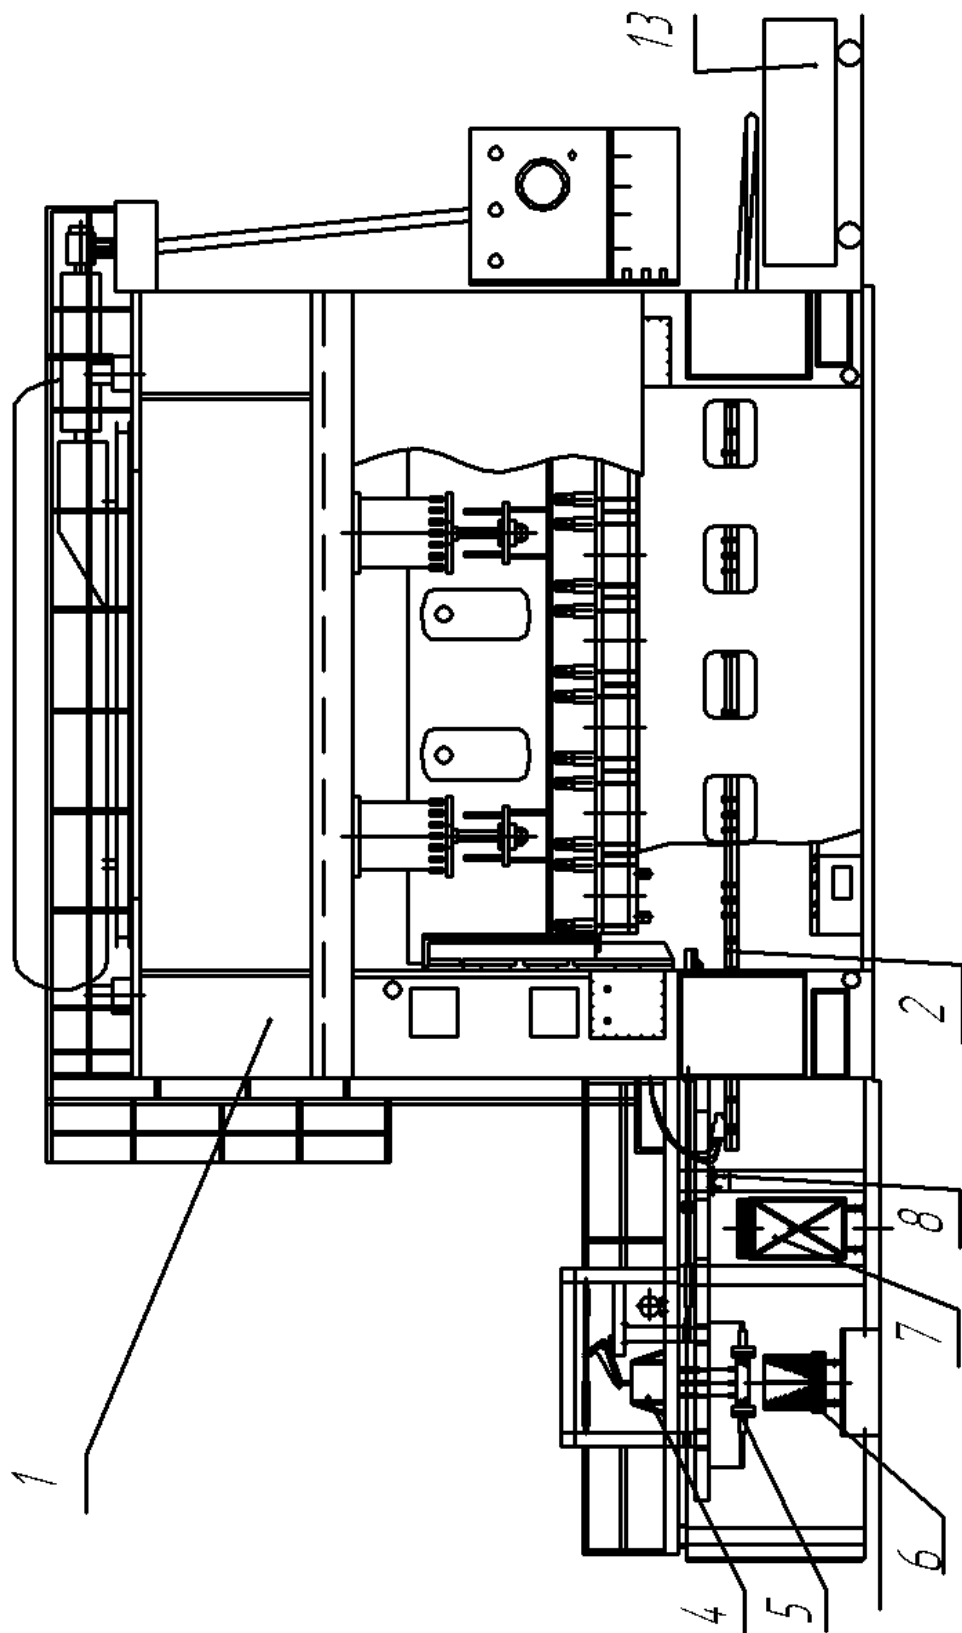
Многопозиционный пресс-автомат Muller Weingarten – 1700
